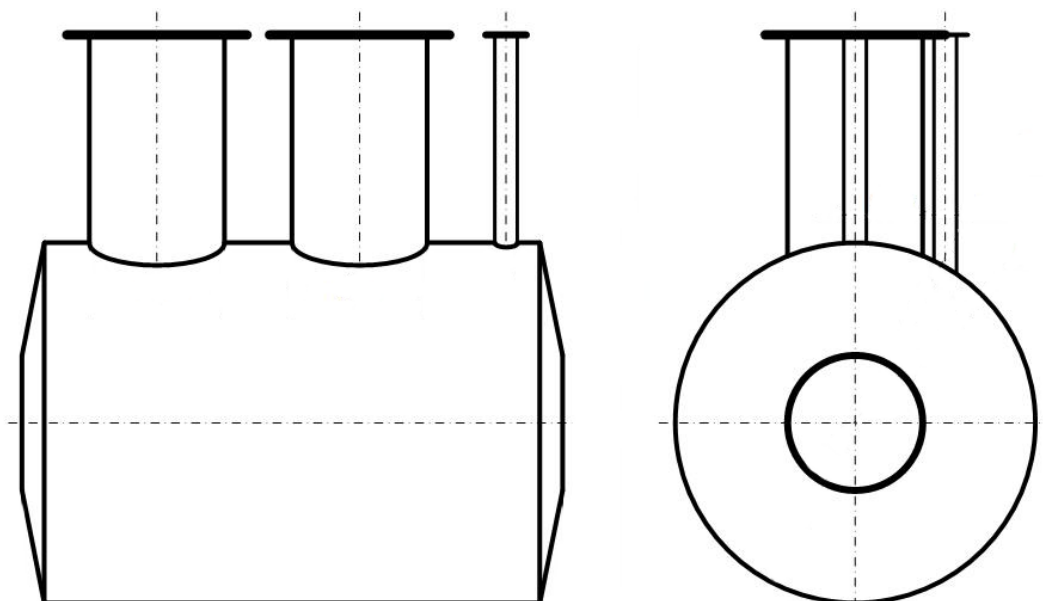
Общий вид эскиза резервуаров РГС-8
